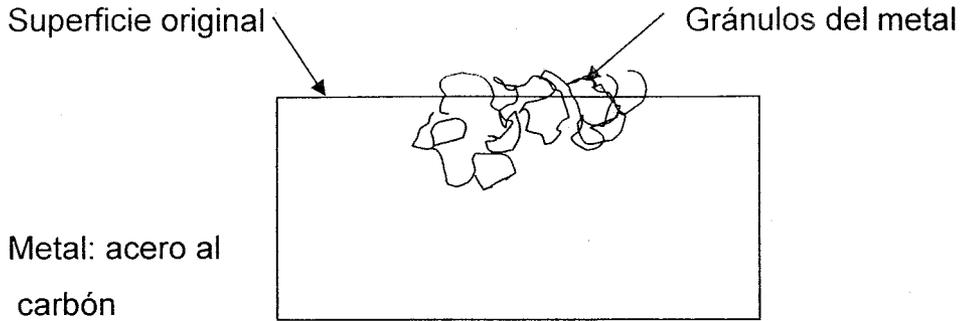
Corrosión intergranular: Se puede presentar en la unión de dos metales mediante soldadura debido a la alta temperatura al ser soldadas.
